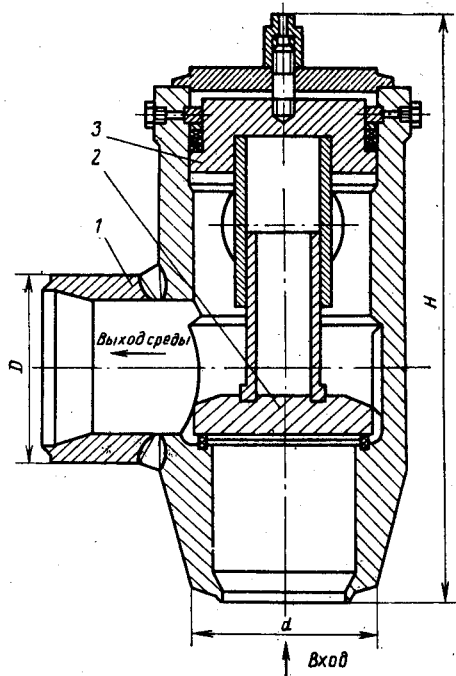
Обратный затвор для автоматической защиты ПВД:
